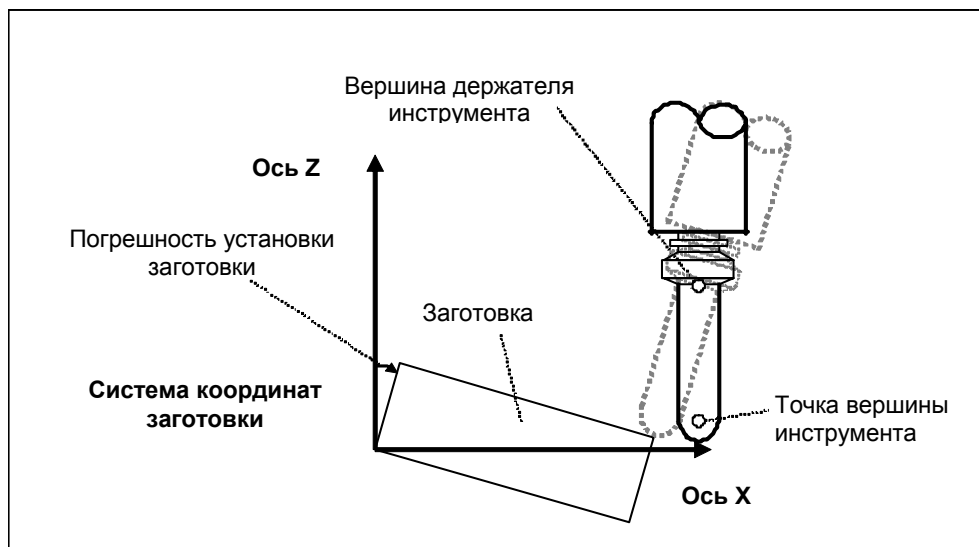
(к) Если присутствует погрешность установки заготовки (Если RCM=0)
